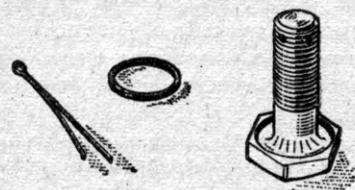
Опытный болт М16 с резиновым кольцом и шпилькой для соединения опорного стакана редуктора с упорной крышкой
